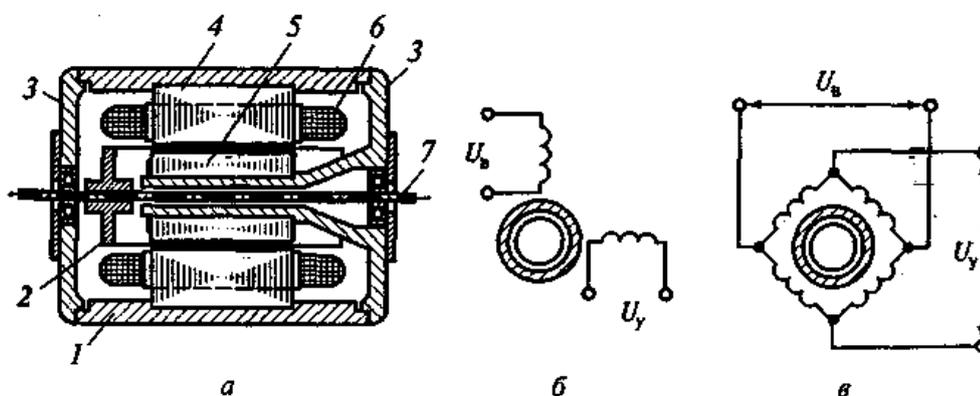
Конструкция асинхронного исполнительного двигателя с полым немагнитным ротором:
